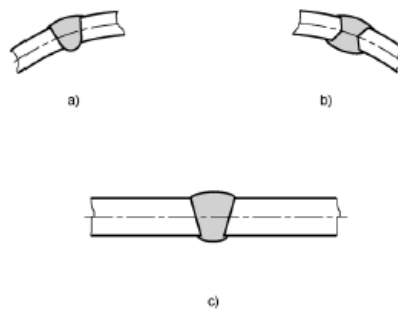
Soldadura de juntas a tope de espesor similar
